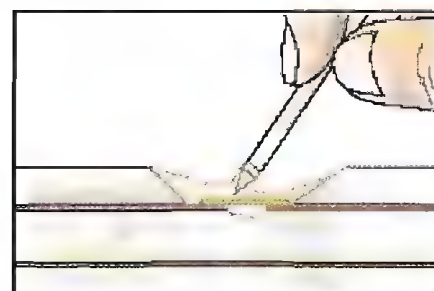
Покрывать верхнюю и боковые стороны нового соединения эпоксидной смолой
